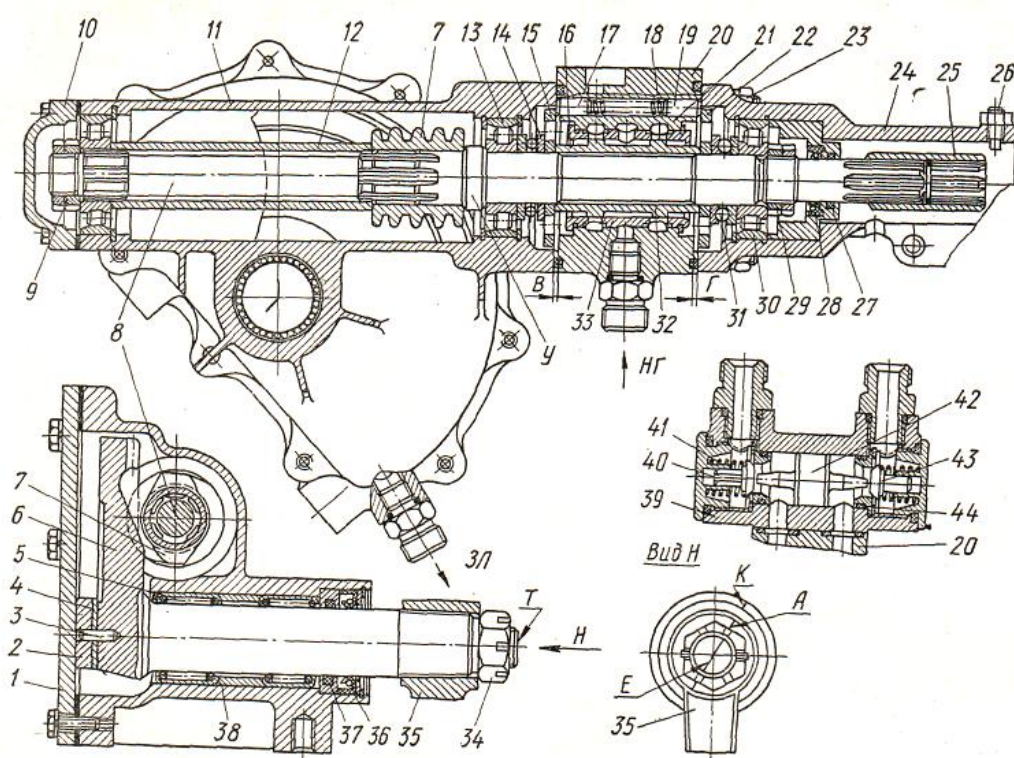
Рульовий механізм: 1 — бічна кришка; 2 — упорна шайба; 3 — штифт; 4 — регульовальна шайба; 5 — голчастий підшипник; 6 — сектор з валом сошки; 7 — черв'як; 8 — вал рульового механізму; 9, 29 і 34 — гайки; 10 24 — нижня і верхня кришки; 11 — картер; 12 і 38 — дистанційні втулки; 13 і
